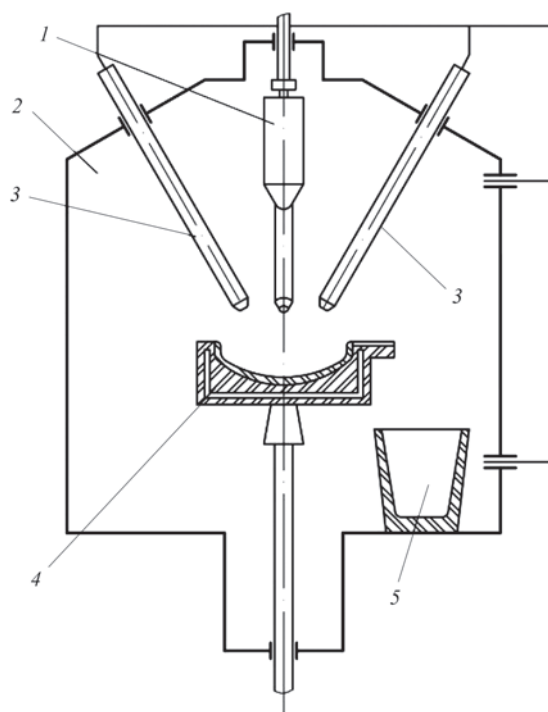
Принципова схема плазово-дугової установки УПГ-1Л: 1 — витратна заготовка; 2 — камера печі; 3 — плазмотрони ПДМ-7; 4 — тигель; 5 — виливниця
